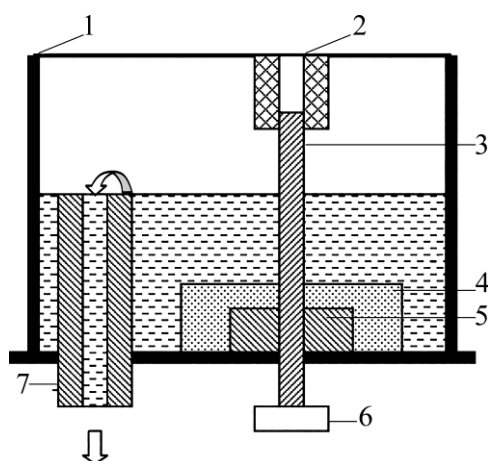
Устройство ПЭХТО с механизированной подачей деталей в зону обработки: 1 – крышка ванны; 2 – втулка; 3 – обрабатываемая деталь; 4 – капроновая шайба; 5 – постоянный катод; 6 – упор; 7 – сливной патрубок [124].
